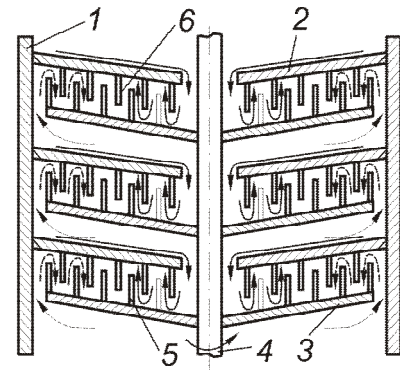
Апарат конструкції В.С. Ніколаєва: 1 – корпус; 2 – нерухома тарілка; 3 – обертова тарілка; 4 – вал; 5, 6 – перегородки
